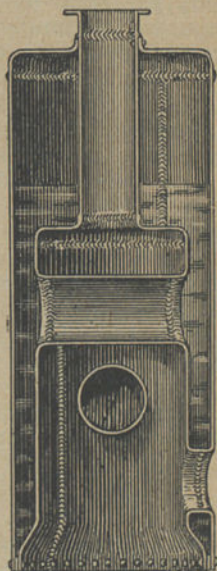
Caldeira inteiramente construída por soldadura autogenea.
